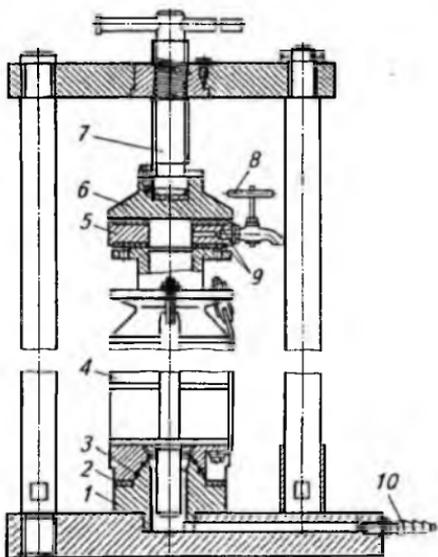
Схема стенда для испытания погружных насосов на герметичность:
